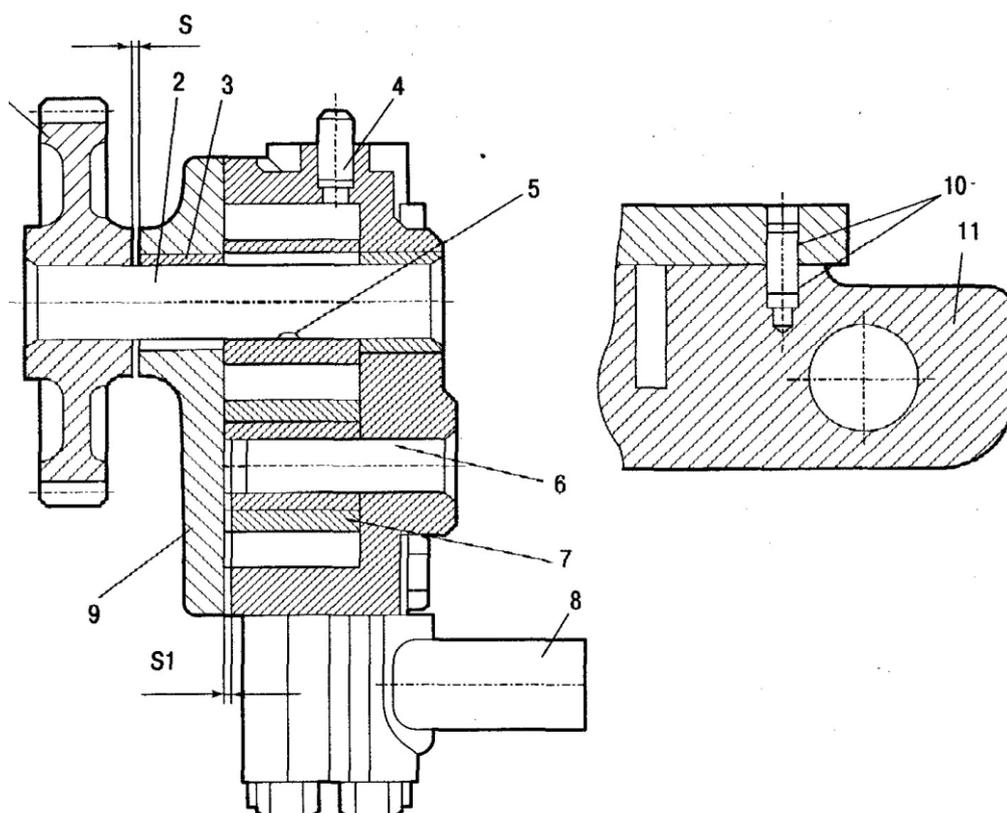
Масляный насос: 1 - шестерня привода насоса; 2 - валик насоса; 3 - втулка; 4, 10 - штифты; 5 - ведущая шестерня; 6 - палец; 7 - ведомая шестерня; 8 - трубка маслоприемника; 9 - крышка; 11 - корпус насоса; S, S1 - зазоры
